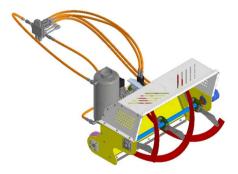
Общий вид рабочего органа подталкивателя-разрыхлителя кормов полунавесного ПКП-0,9
